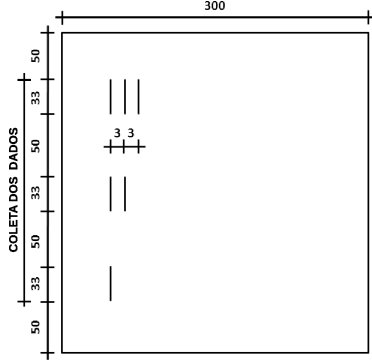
Corpo de prova utilizado com dimensões em milímetros. Adaptado de Silva et al. [2].
